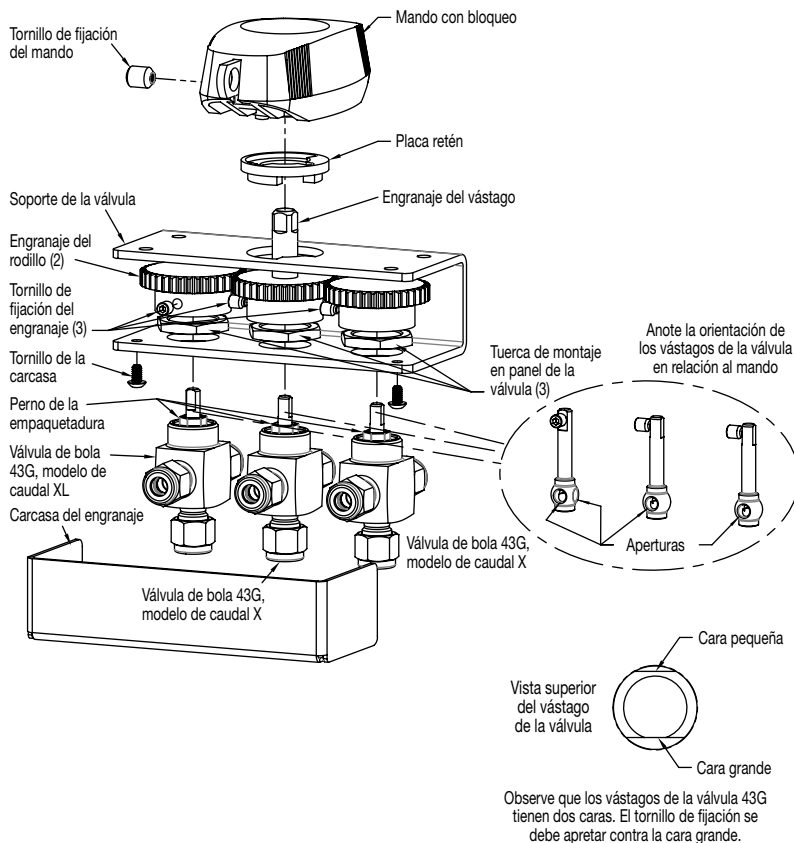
Despiece del ensamblaje de 3 Válvulas GSM
